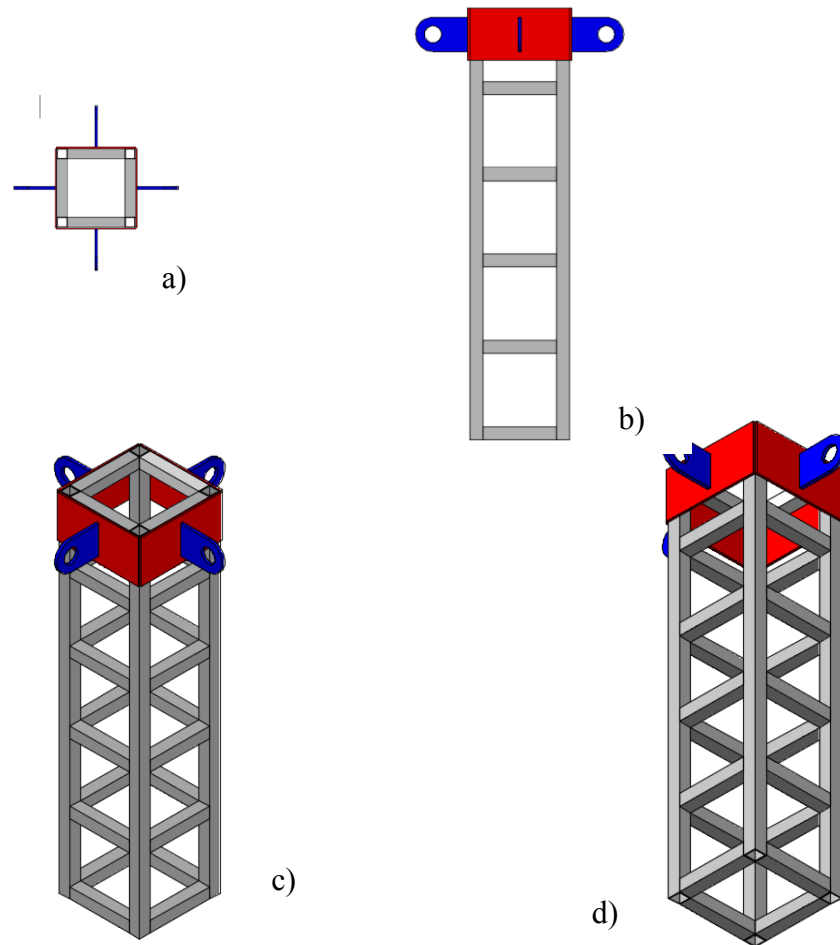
a) Planta de torre. b) Elevación de torre. c y d) Isométrico de torre.
